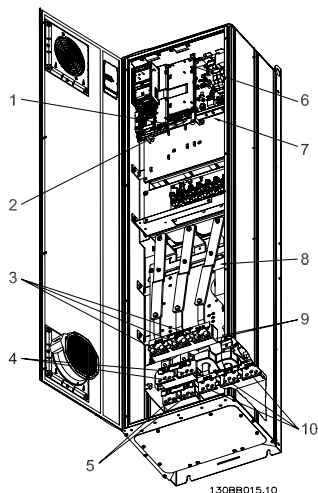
Compact IP 21 (NEMA 1) и IP 54 (NEMA 12), размер корпуса D1
